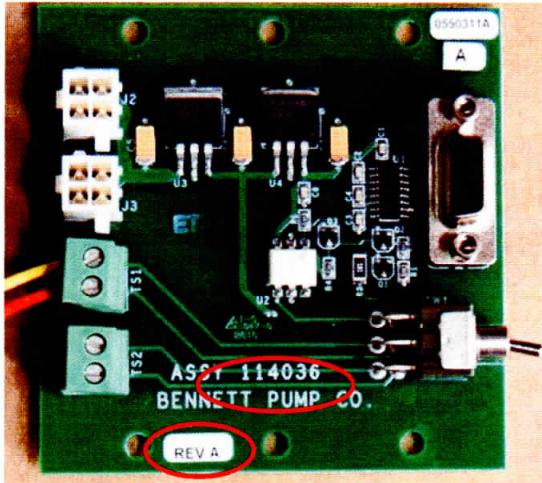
Tarjeta Circuit Board Assy Mexico RS-232 Port identificada con número de parte 114036 REV A, vista cara de soldaduras.
